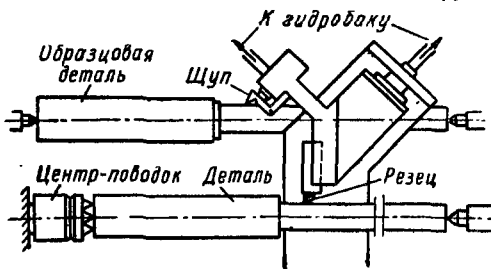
Схема обработки двухступенчатого валика с помощью гидросуппорта КСТ-1.
